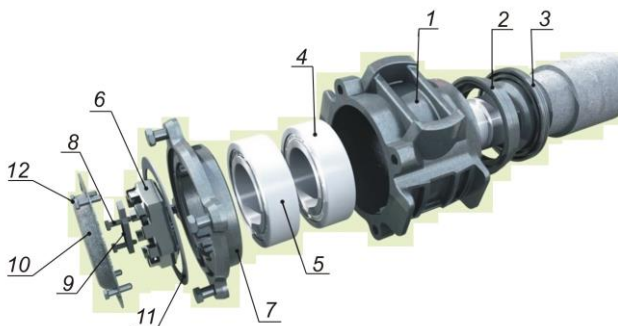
К монтажу типового буксового узла с цилиндрическими подшипниками:
